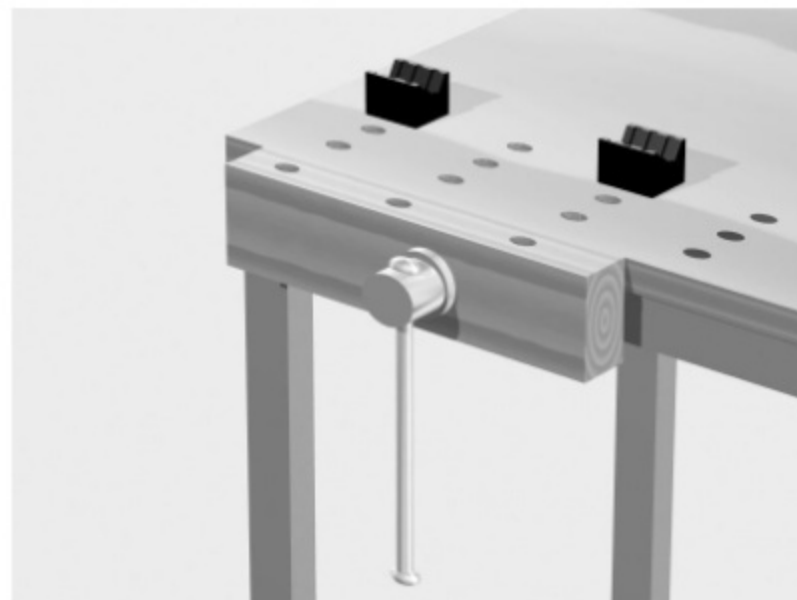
Detalle de una prensa horizontal en un banco de bricolaje
